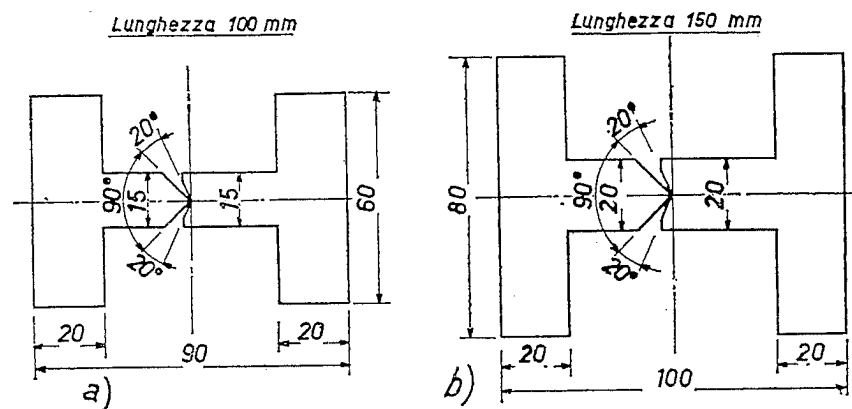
Cerniere per provetta: a) tipo A - b) tipo B.
